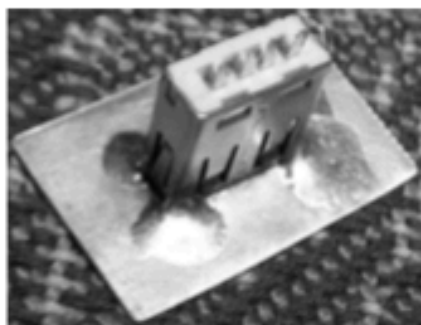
Выпиленная по размерам части USB-соединителя рамка из белой жести одета на его корпус и припаяна в углах
